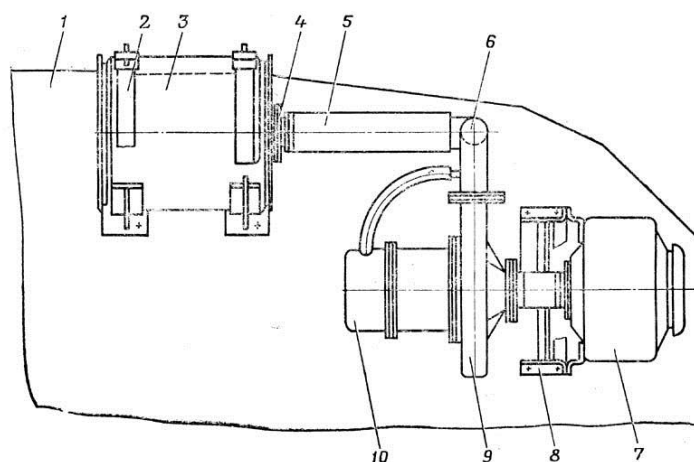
Фильтровентиляционная установка: 1 – каркасный металлический кузов КМ-131; 2 – лента в сборе; 3 – изделие ФПТ-200М; 4 – патрубок с фланцем; 5 – дюритовый шланг; 6 – колено с фланцем; 7 – предфильтр ПФА-75М; 8 – кронштейн; 9 – электровентилятор; 10 – кожух в сборе.
